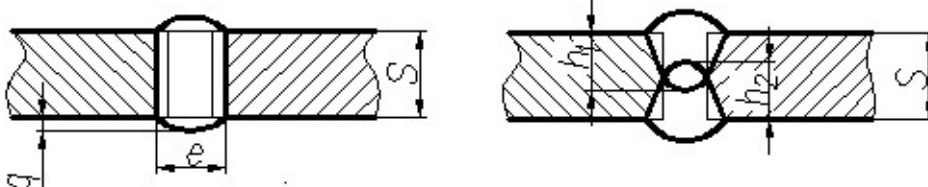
Односторонняя сварка. Рисунок 8 - Двусторонняя сварка.
